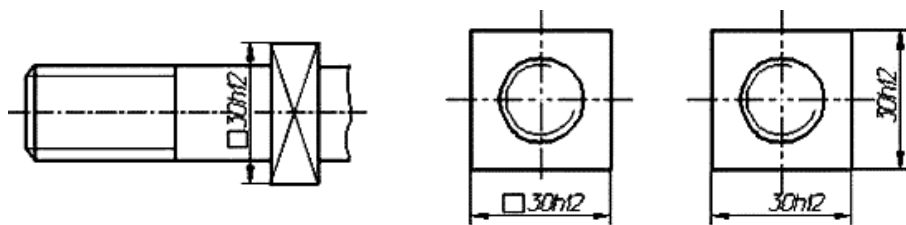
Примеры нанесения размера с использованием знака «квадрат»
